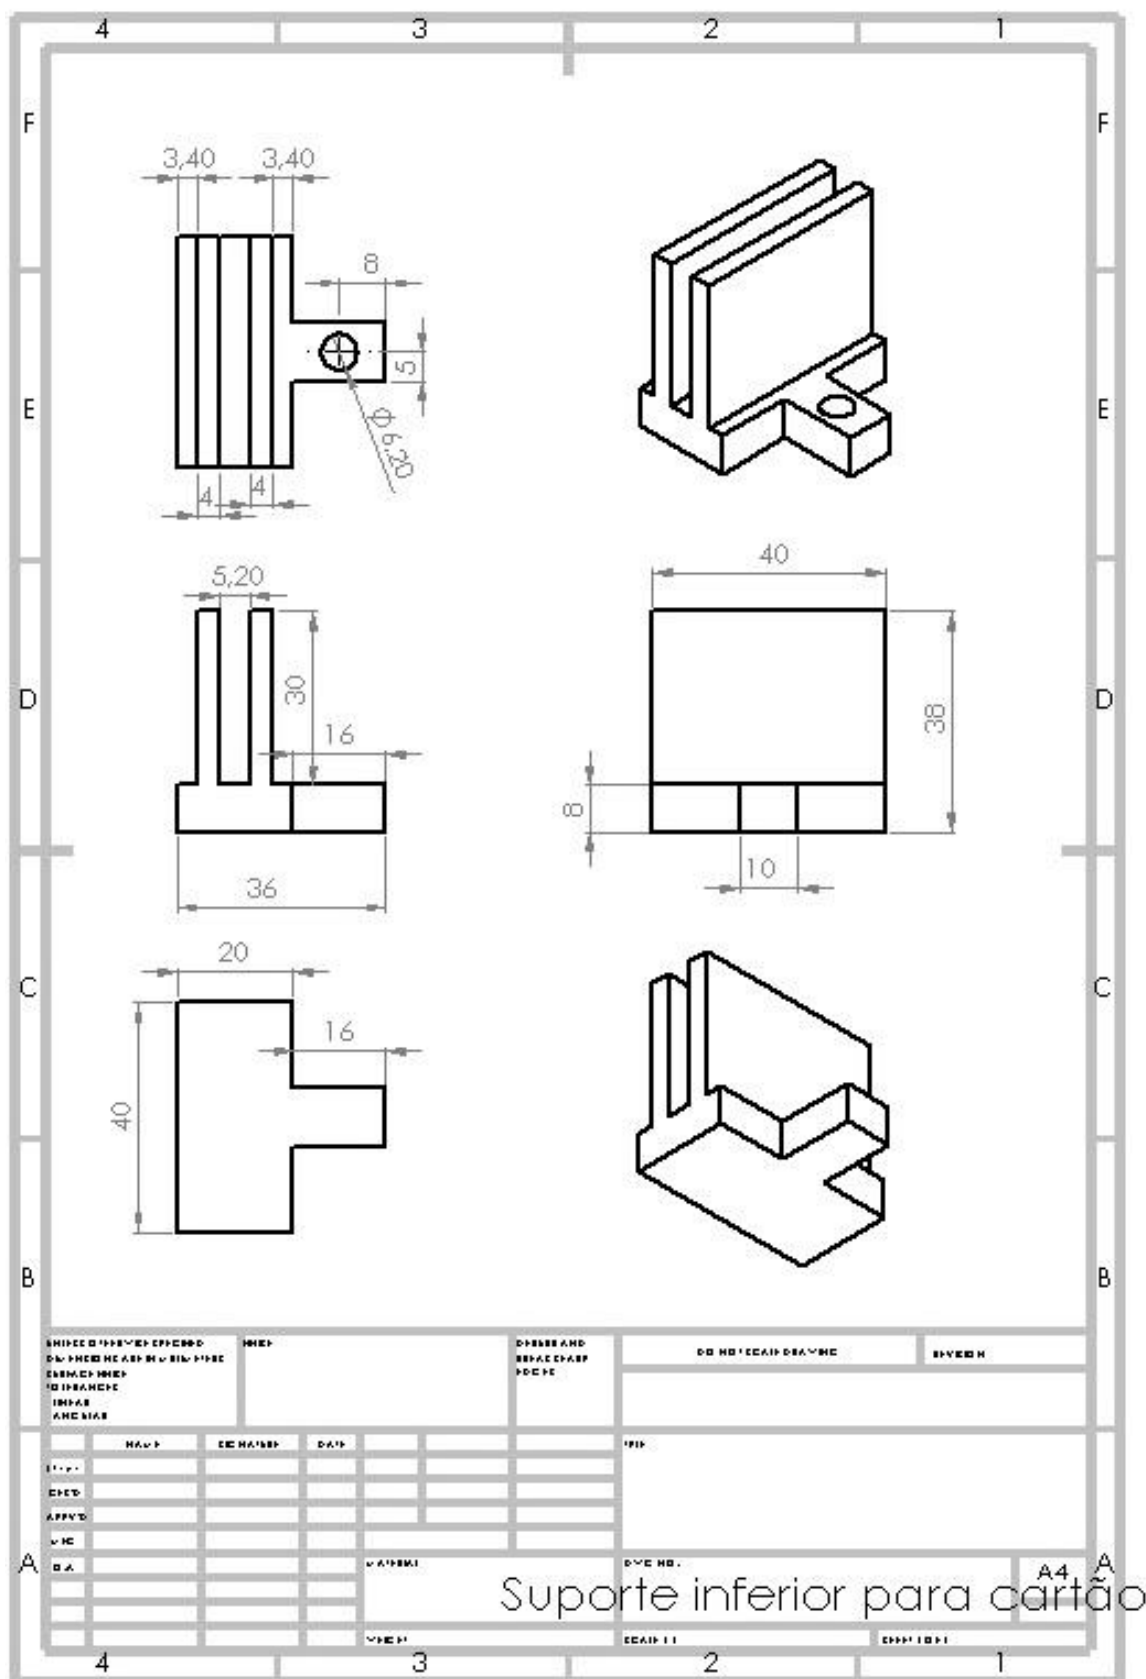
Desenho técnico da peça Suporte inferior para cartão
